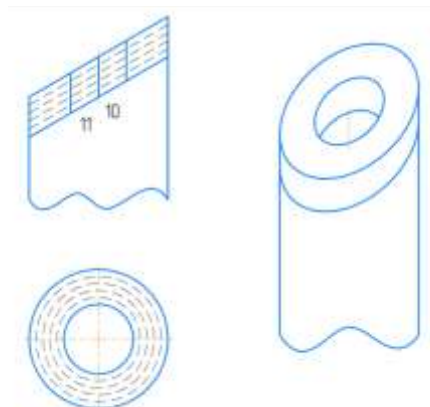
Эскиз трубы с наплавкой И АМ 117.03.02.540 [Sketch of a tube with cladding AND AM 117.03.02.540]
